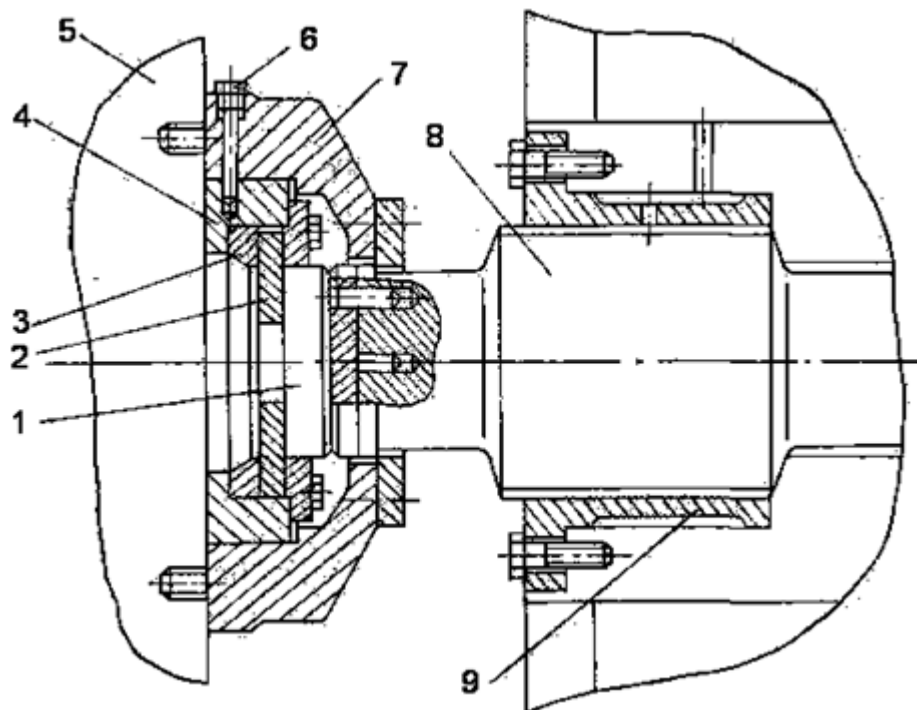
Запобіжна шайба корпусу підшипника валка: 1 – пуансон-підп'ятник; 2 – запобіжна шайба; 3 – опорна шайба; 4 – касета; 5 – корпус підшипника валка; 6 – гвинт; 7 – корпус касети; 8 – натискний гвинт; 9 – гайка
